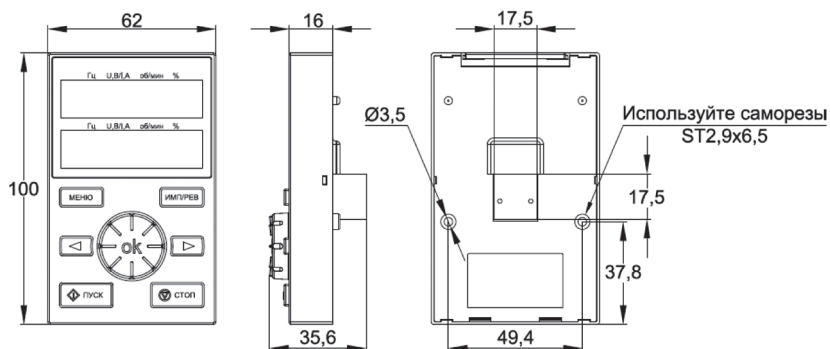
Габаритные размеры и размеры отверстий внешней цифровой двухстрочной панели управления (единица измерения – мм)
